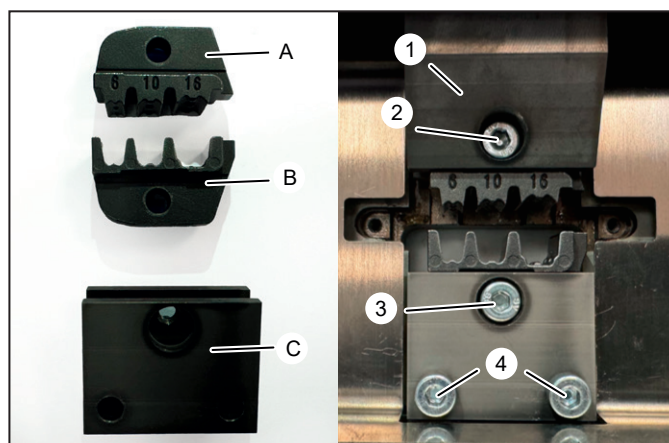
Crimpeinsatz für Kabelschuhe mit Einlagehilfe
